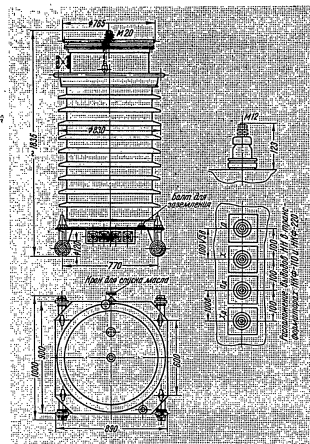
Габаритные размеры трансформатора напряжения типа НКФ-110
